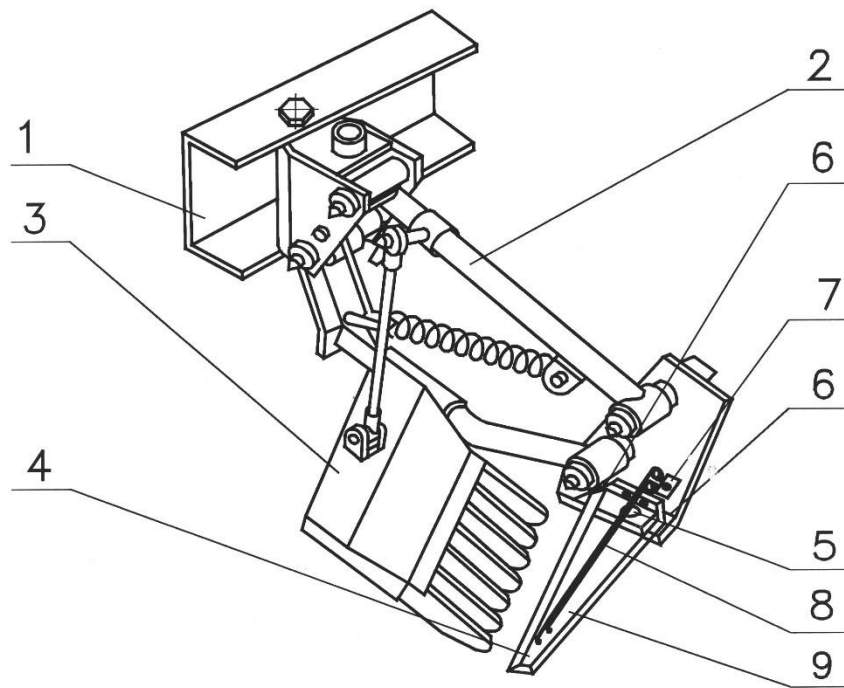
Конструктивна схема гичкозрізувального пристрою з підпружиненим ножом:
